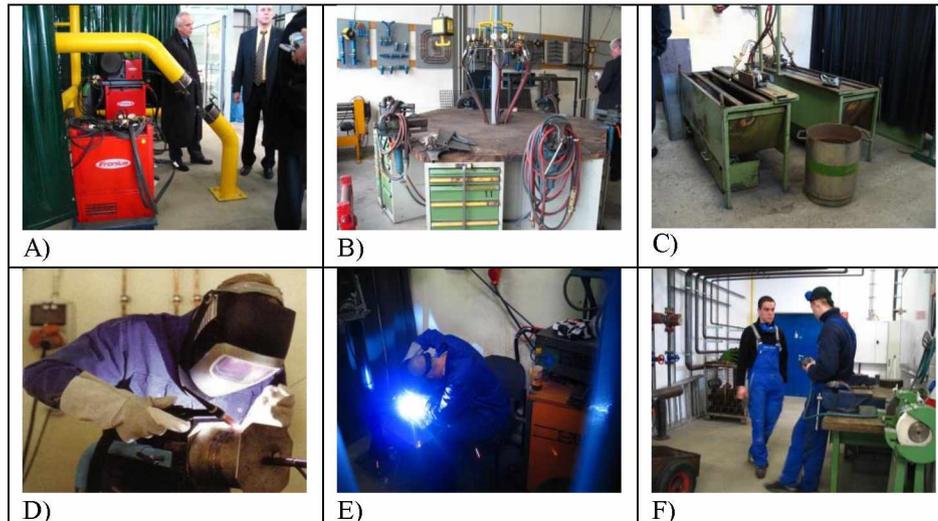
A- MIG/MAG - Anlage, B- Gasschweiß-Arbeitsplatz, C - Brennertisch, D - WIG-Schweißer, E - MIG/MAG, F - Pausengespräch
